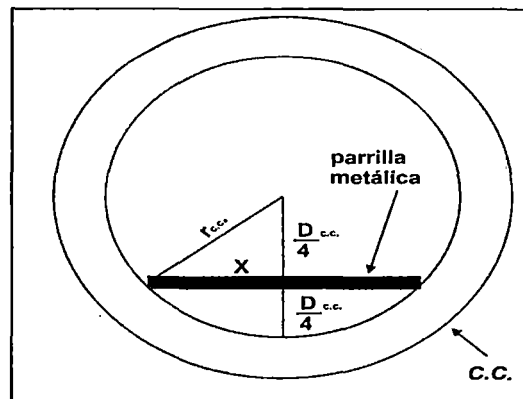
Diagrama para el cálculo del ancho de la parrilla metálica.
